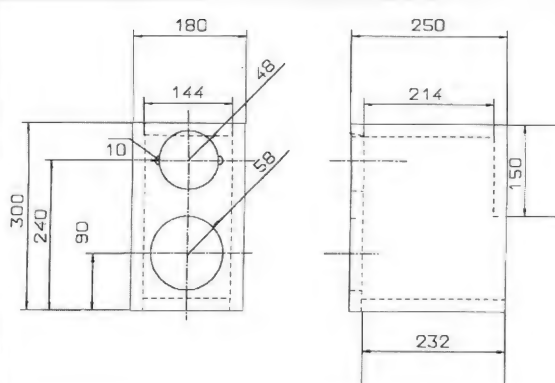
Vooraanzicht wooferbehuizing met buitenpanelen
